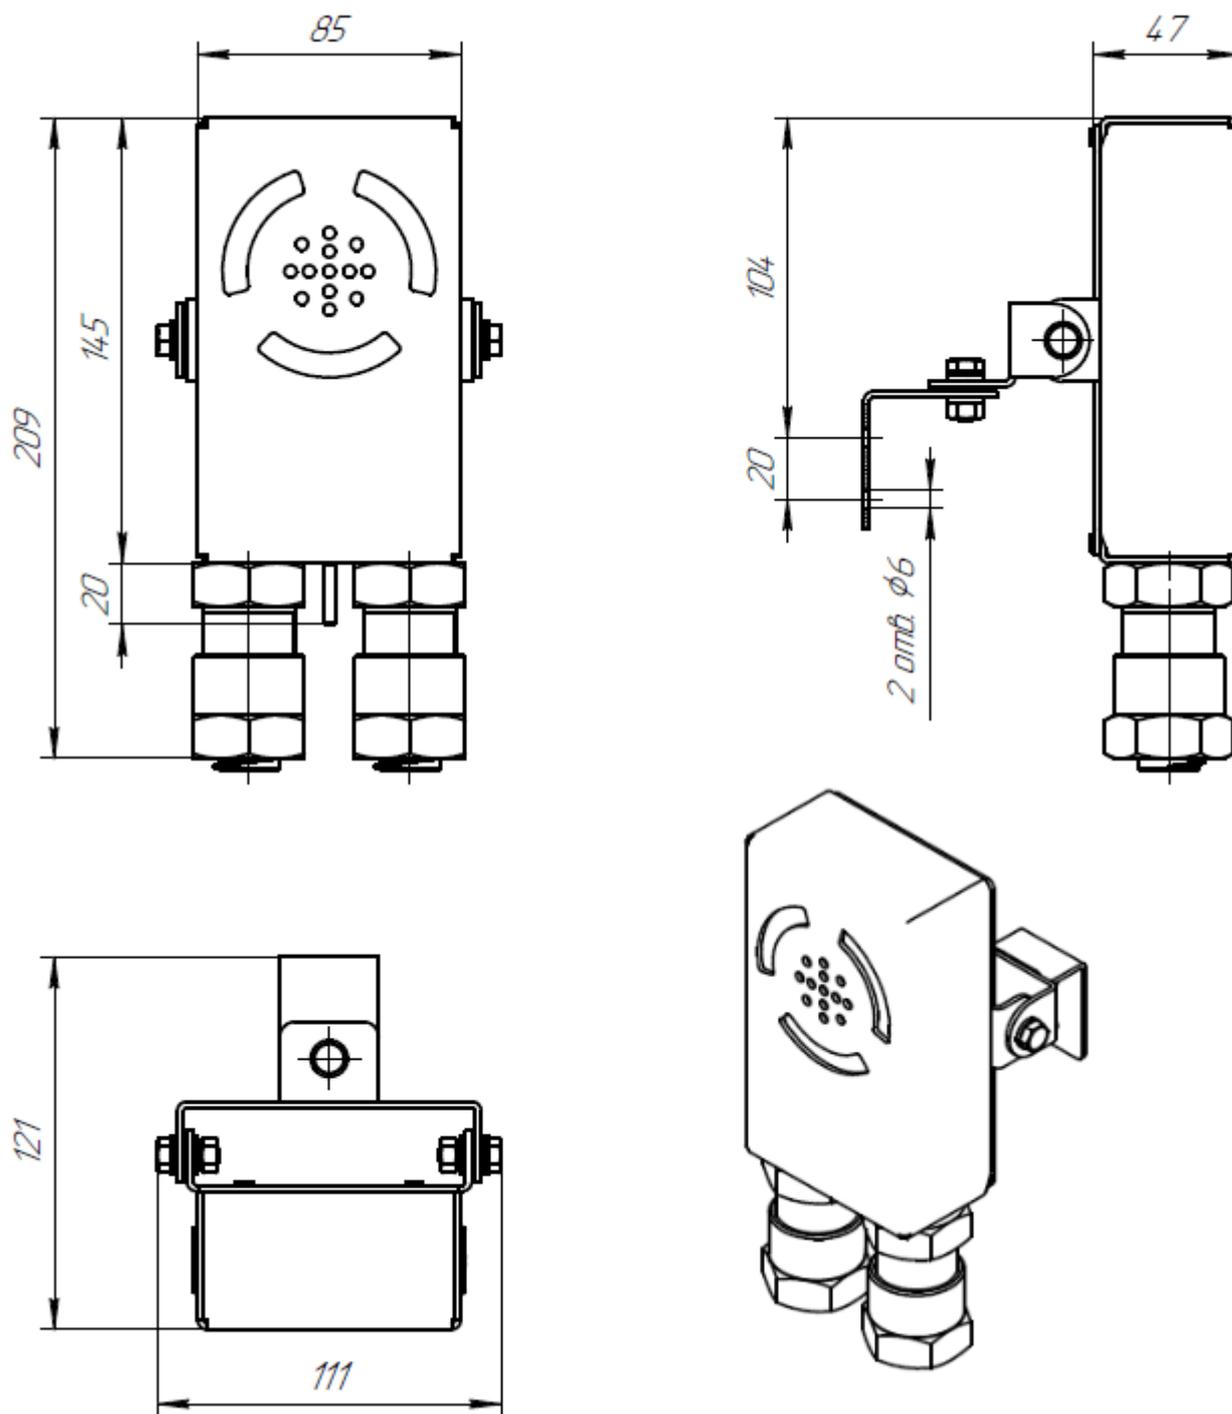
Внешний вид и габаритные размеры светового и комбинированного оповещателя в металлическом корпусе
